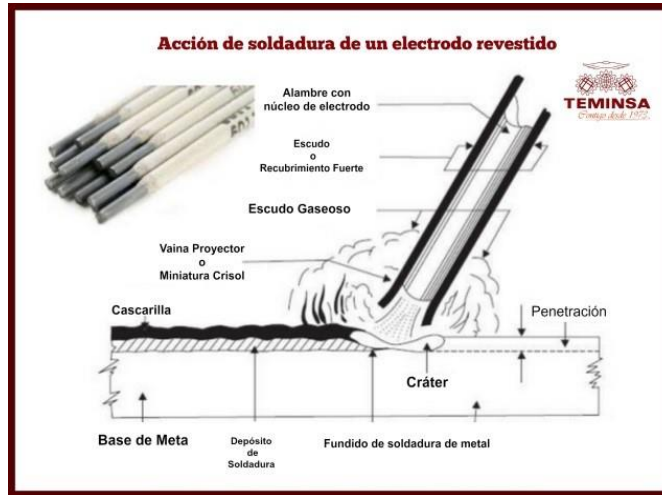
Equipo de soldadura de arco metálico protegido.
